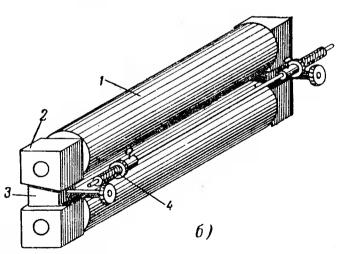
Схема станка для смятия (закатки) заусенцев.
